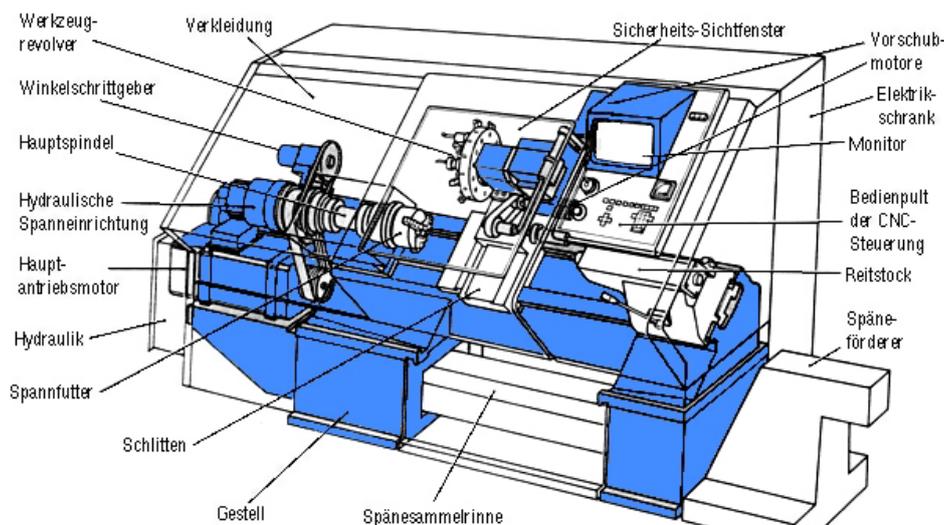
Aufbau einer CNC- Drehmaschine; Quelle: Internet
